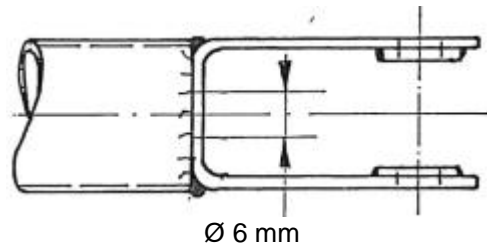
Skizze der Kontrollbohrung am Gabelkopfende (Bohrung Ø 6 mm), geschweißte Version
